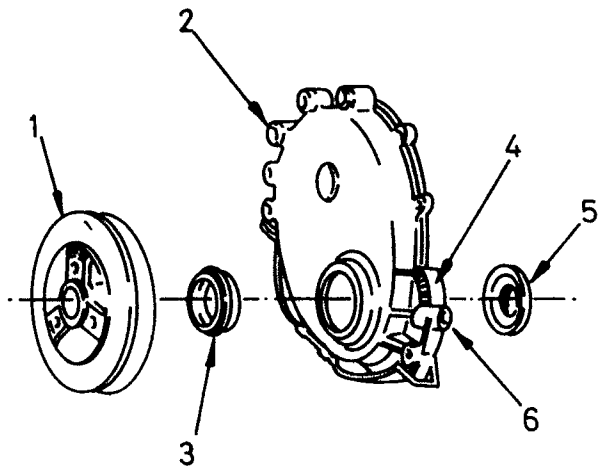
Die Teile des Steuerdeckels beim Sechszylindermotor.
